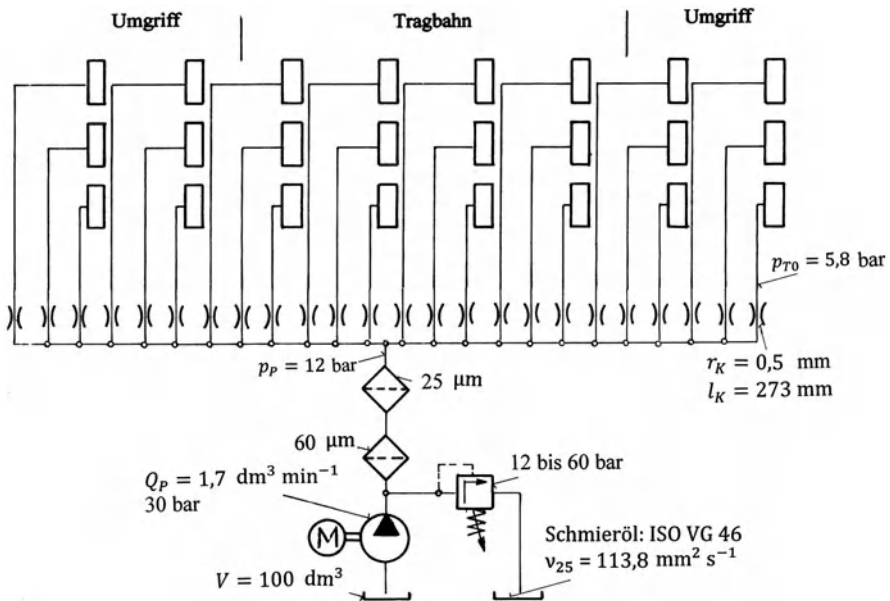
Hydraulikplan für die zentrisch belasteten hydrostatischen Führung mit Umgriff mit Ölversorgung durch 24 einzelnen Kapillardrosseln
